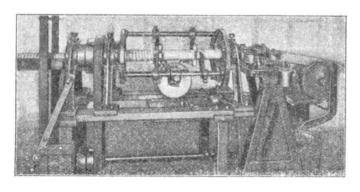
Maschine zum Umwickeln des Schlauches mit Draht.
